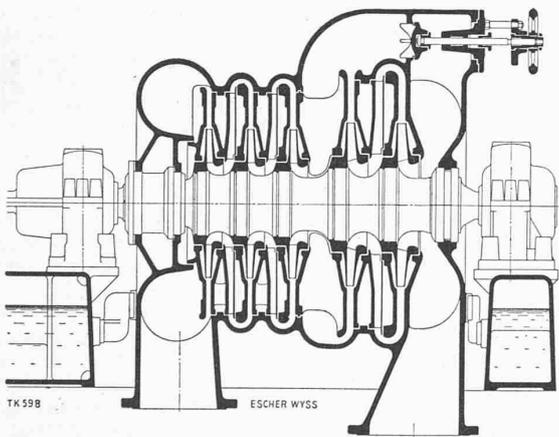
Turbokompressor mit Handventil zur Umgehung
